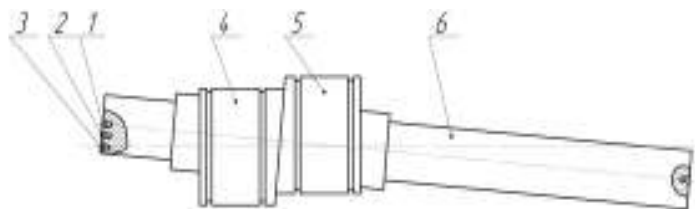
Эксцентриковый вал волновой передачи с промежуточными телами качения
